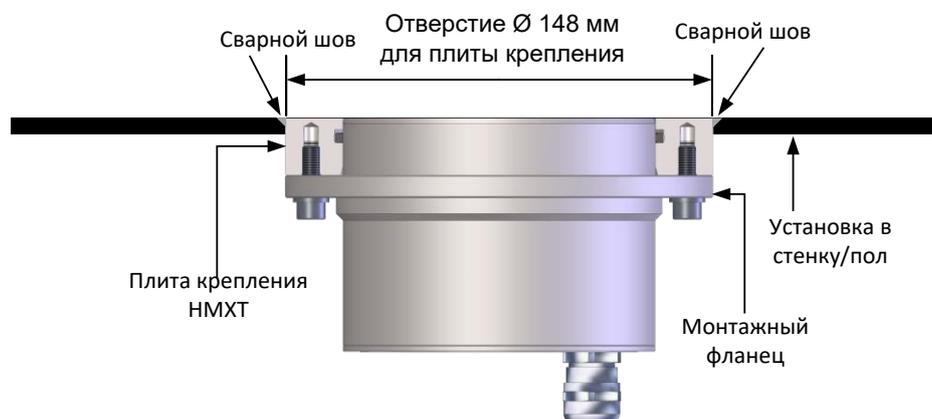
Установка датчика (монтаж плиты крепления заподлицо)
